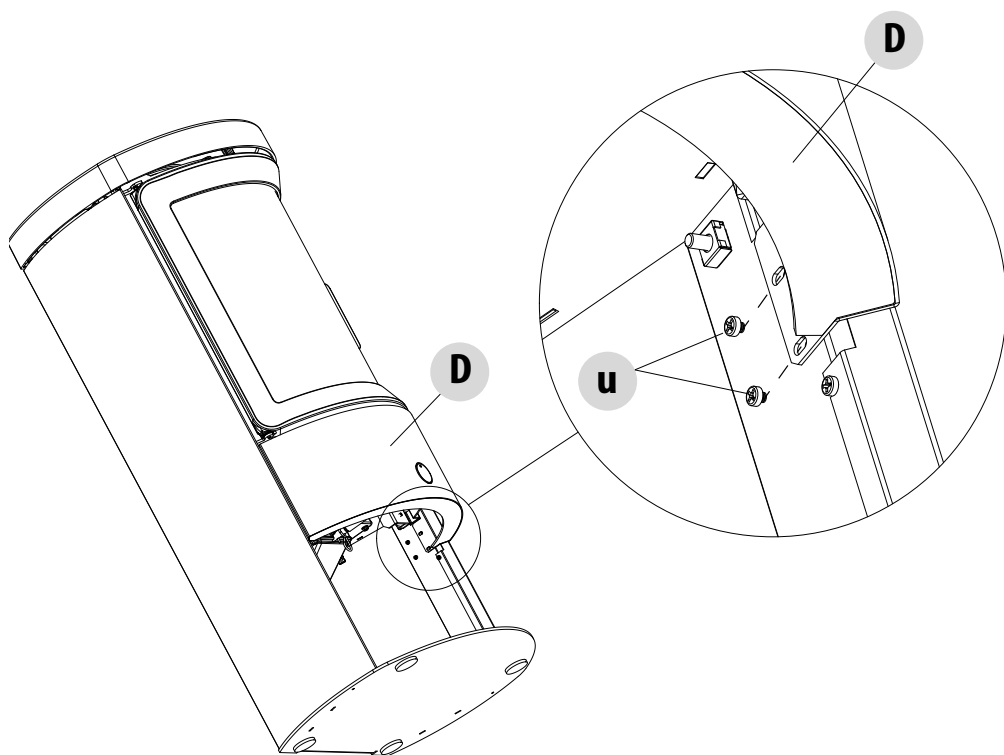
SMONTAGGIO PANNELLO FRONTALE
